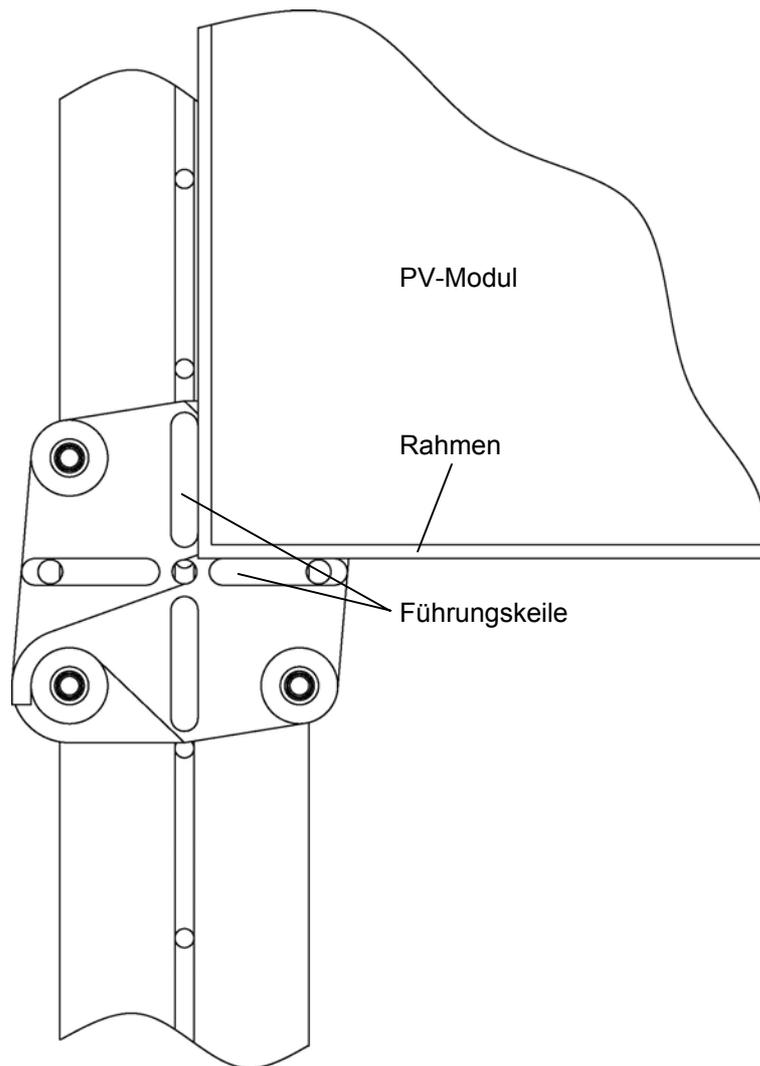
Modulverbinder als Viererstecker mit einem gerahmten PV-Modul
